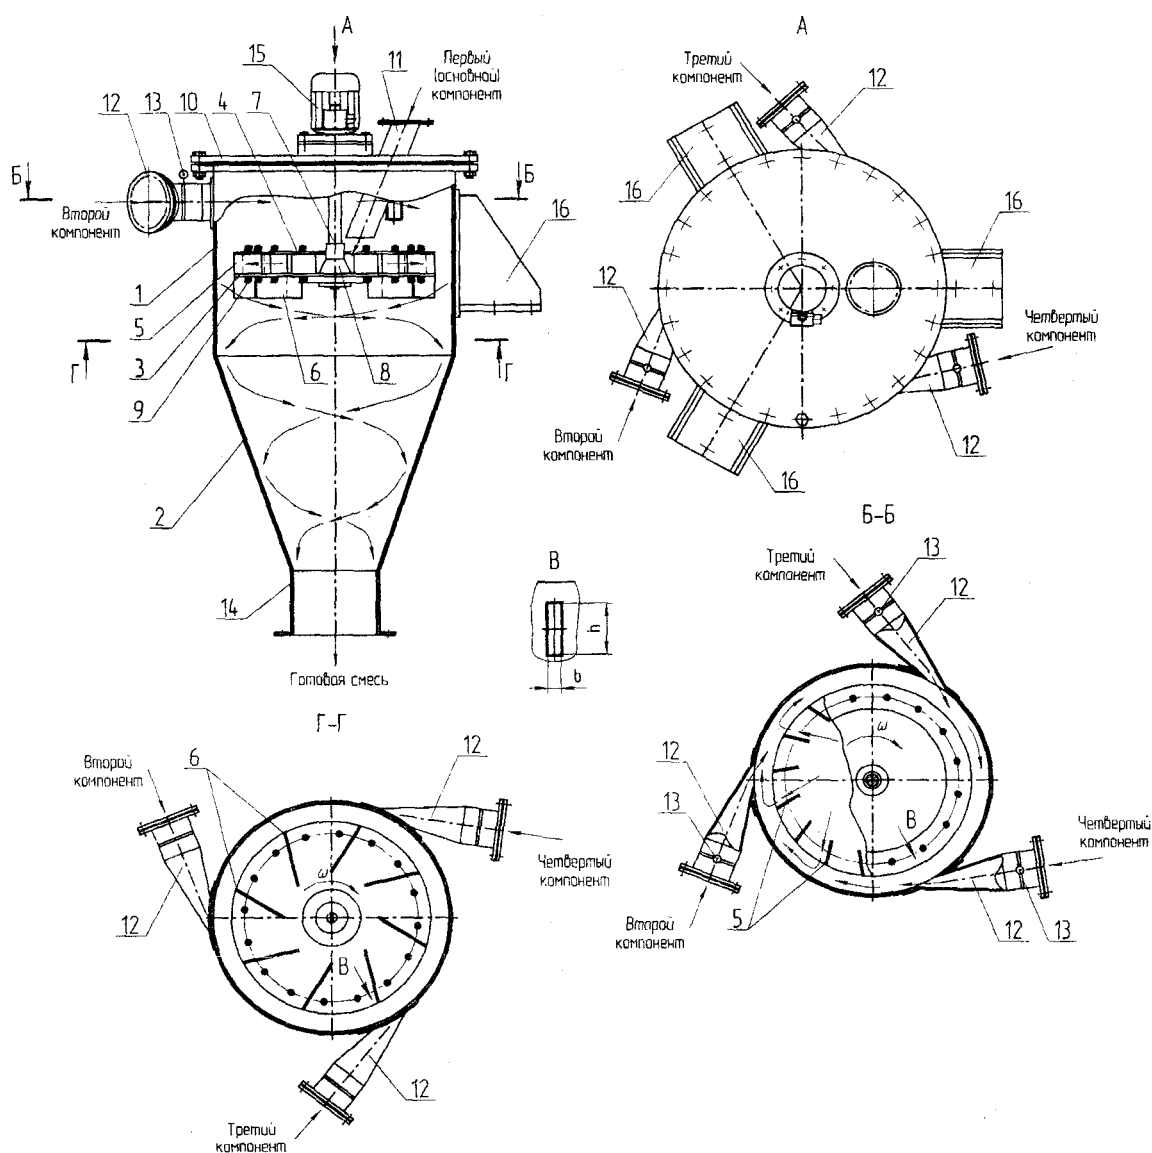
Роторно-центробежный смеситель с дополнительными вентиляторными лопатками
